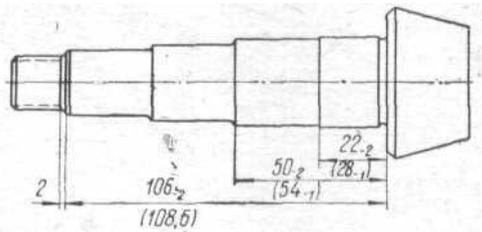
Размеры (без скобок) для дополнительной обработки вала ведущей шестерни главной передачи
